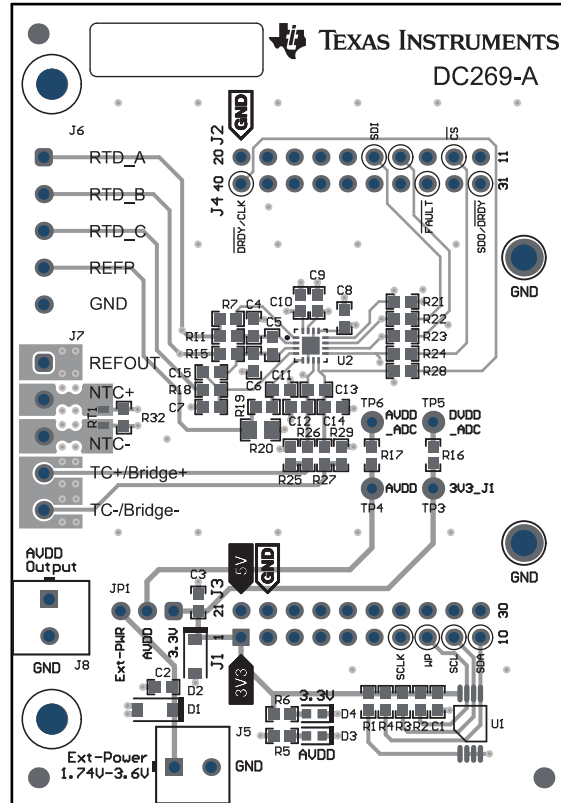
ADS122x14EVM 的 PCB 布局 (顶视图)
